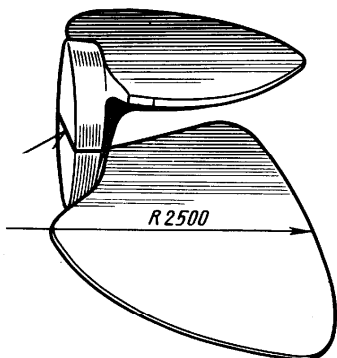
Сварно-литая лопасть рабочего колеса двуперовой турбины
